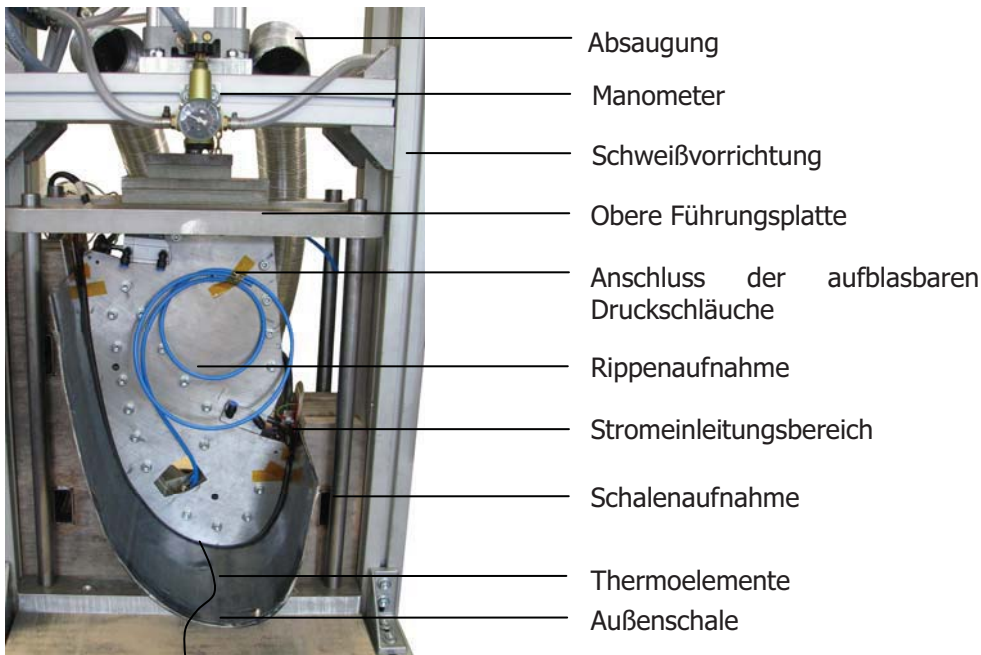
Prozessaufbau für den Widerstandsschweißprozess des Demonstrators
